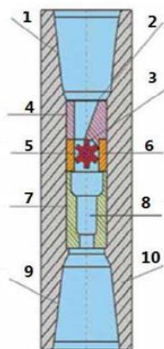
Конструкция ГГИКС, 1 - верхняя соединительная муфта; 2 - эластичная манжета; 3 - рабочее колесо (крыльчатка); 4 - отклоняющее устройство; 5 - вал рабочего колеса; 6 - опора рабочего колеса; 7 - автоколебательная насадка; 8 - полостной резонатор; 9 - нижняя соединительная муфта; 10 - корпус
